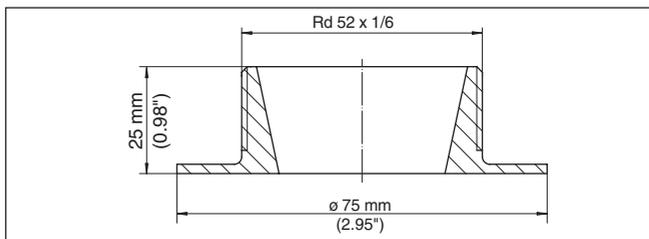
Medidas da luva para soldagem conexão cônica DN 25
